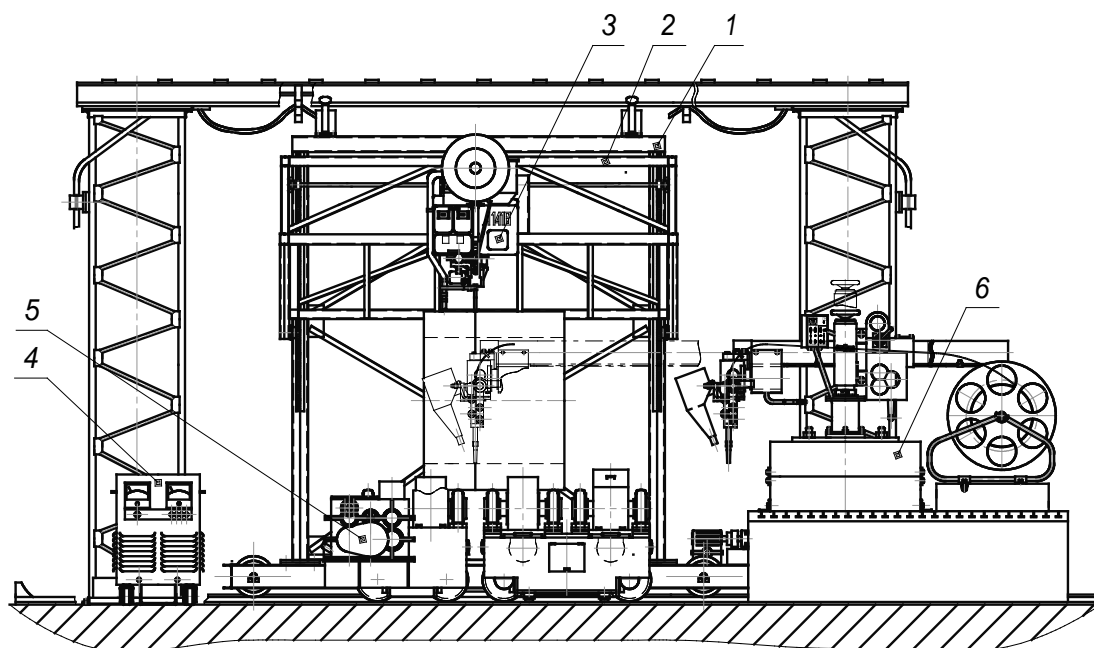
Общий вид установки для сварки кольцевых швов
